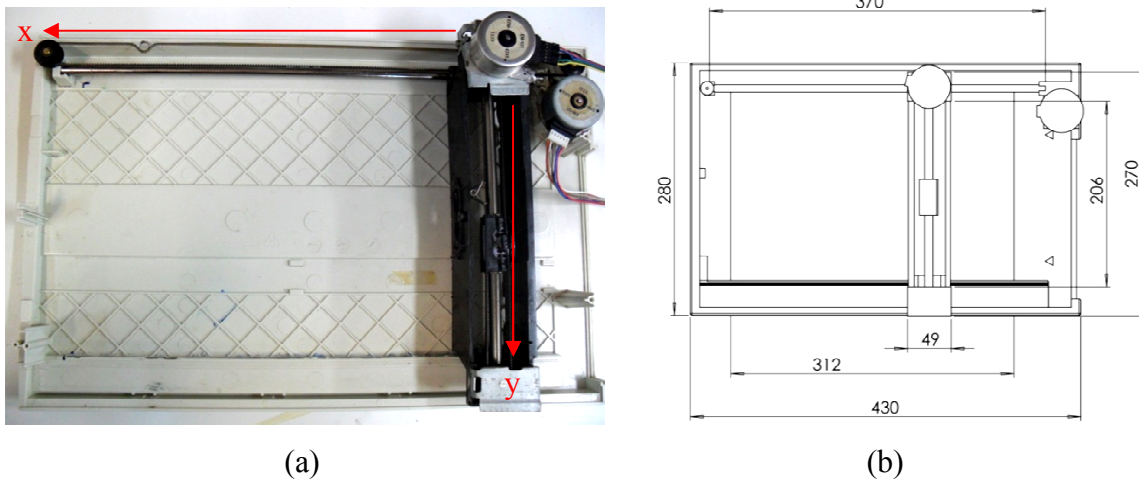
(a) Configuração de montagem dos eixos X-Y; (b) Dimensões básicas (em mm) do protótipo e seus eixos.
